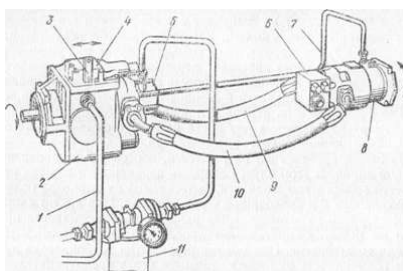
Основные элементы объемного гидропривода с замкнутой циркуляцией: 1, 7, 9, 10 — трубопроводы, 2, 5 — насосы, 3 — рычаг управления, 4 — предохранительный клапан, 6 — коробка, 8 — гидромотор, 11 — фильтр тонкой очистки
